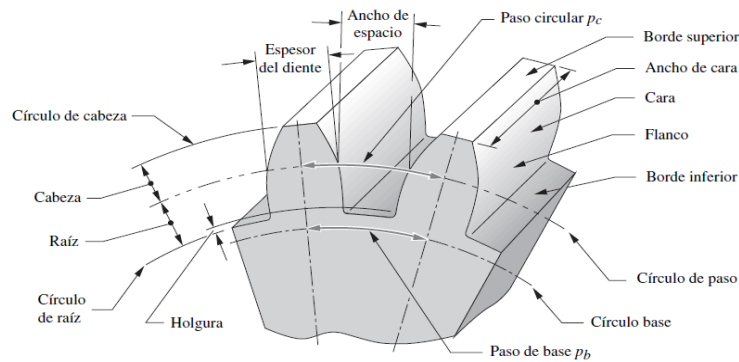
Dimensiones de la geometría de un engranaje [3]
